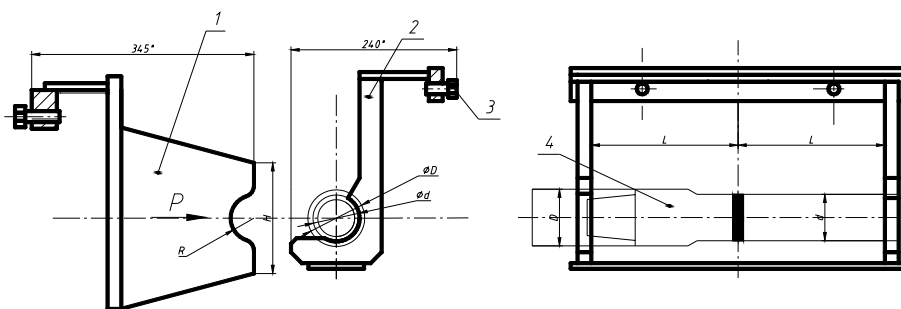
Приставка к разрывной машине ДЗБО для испытания труб на изгиб: а – вид сбоку, указано положение буровой трубы; б – положение сварного шва относительно точки приложения усилия; 1 – упор; 2 – опора; 3 – болты; 4 – испытуемый образец сварного шва
